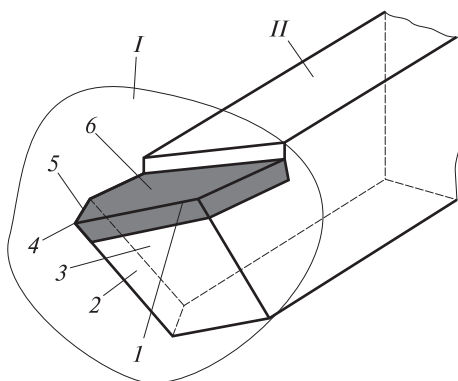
Части (*I*, *II*) и элементы (*1—6*) лезвия токарного резца
